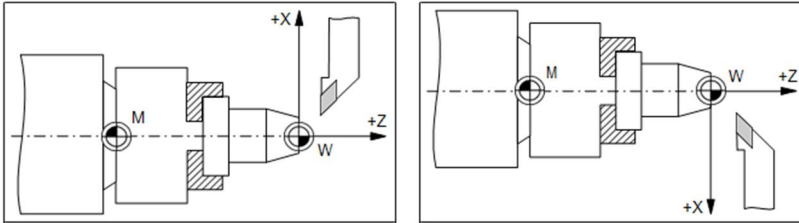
Розташування нульової точки заготовки при роботі на токарному верстаті з ЧПК
